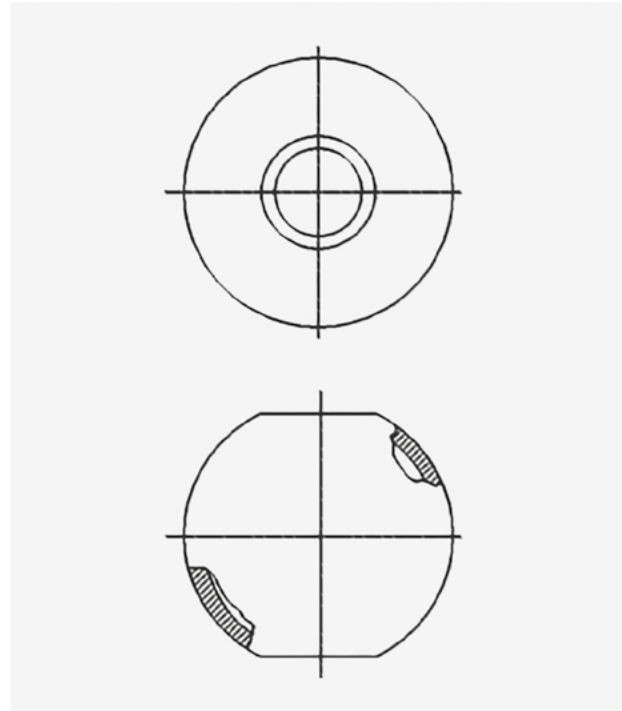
Прочный корпус, склеенный из 2 полусферических заготовок
